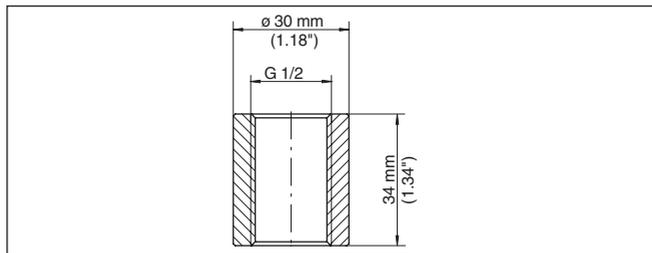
Dimensiones racor para soldar rosca G $\frac{1}{2}$ (EN 837) conexión de manómetro - VEGABAR 81, 82, 83
